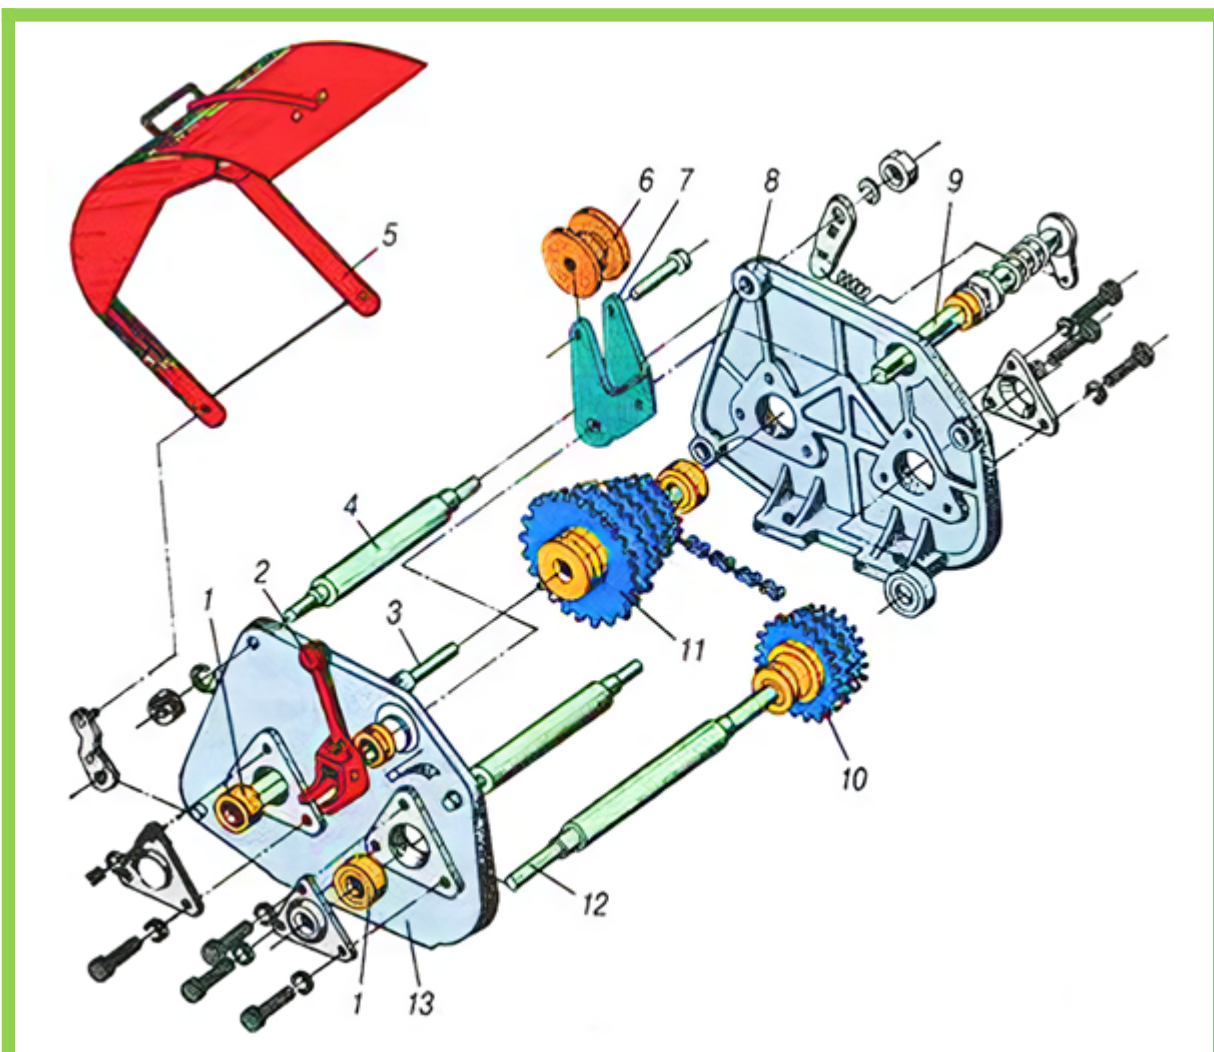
Схема ланцюгового редуктора бурякових сівалок ССТ-12В і ССТ-8В:
